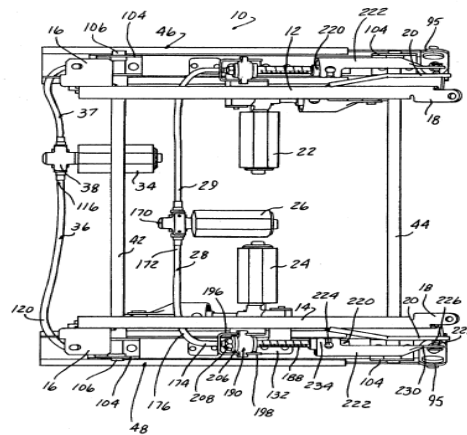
Vista en planta de un ajustador de asiento eléctrico (Patente n° US005467957A).
